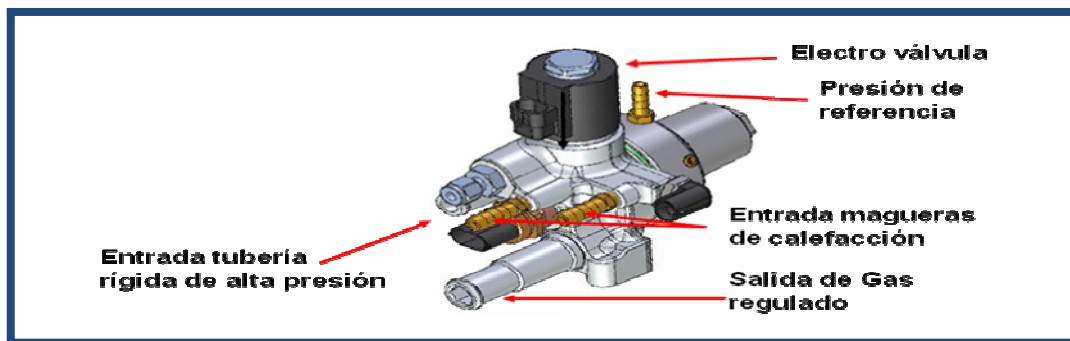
Regulador de presión utilizado en el proceso de conversión mediante la tecnología de presión positiva.
